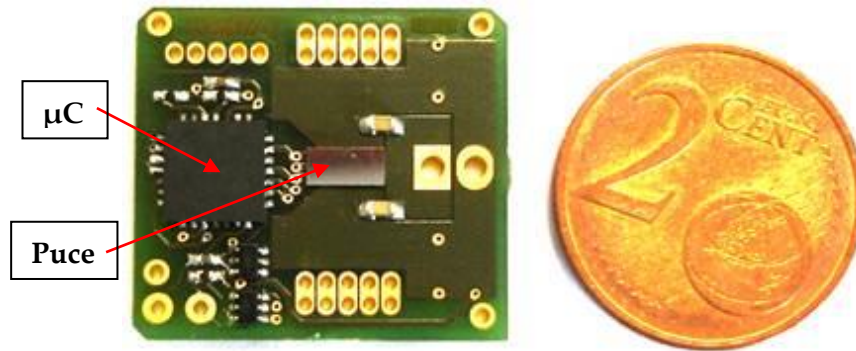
Assemblage flip chip entre la puce et le PCB
